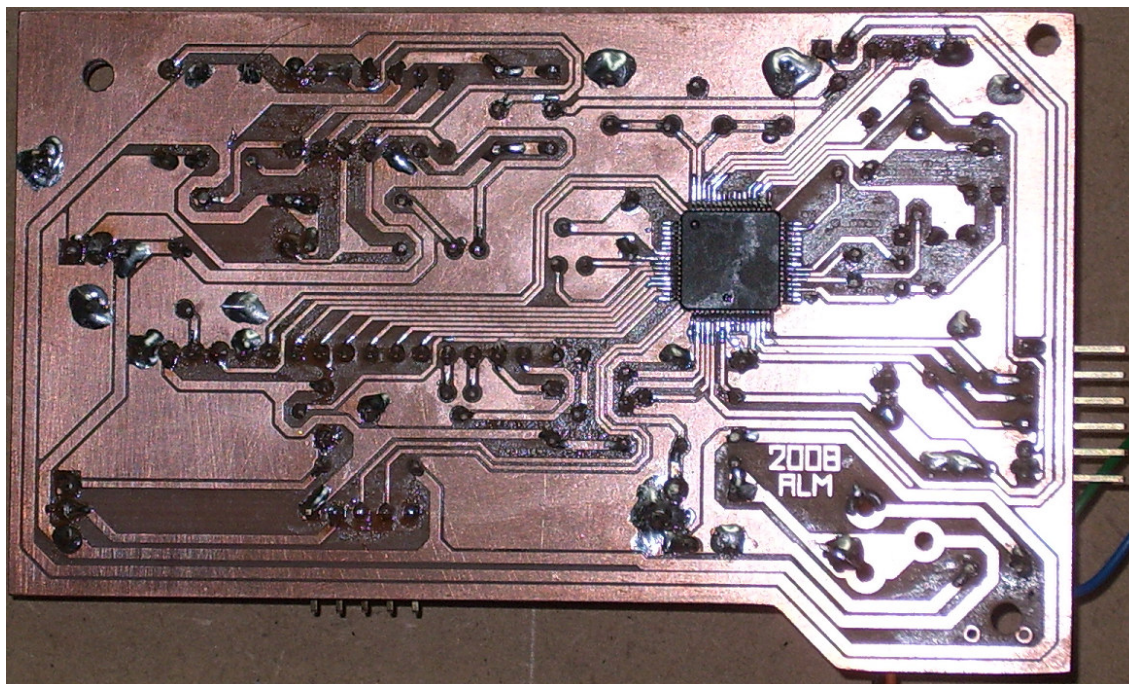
Face inferior da placa do Módulo Móvel (lado das soldas)
